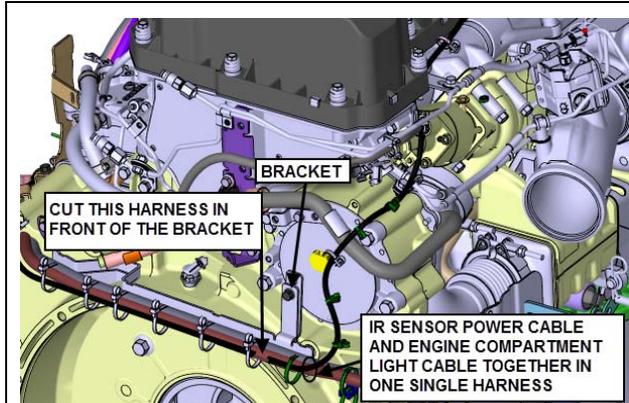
COUPER LE CABLAGE PRÈS DU SUPPORT (BRACKET)
